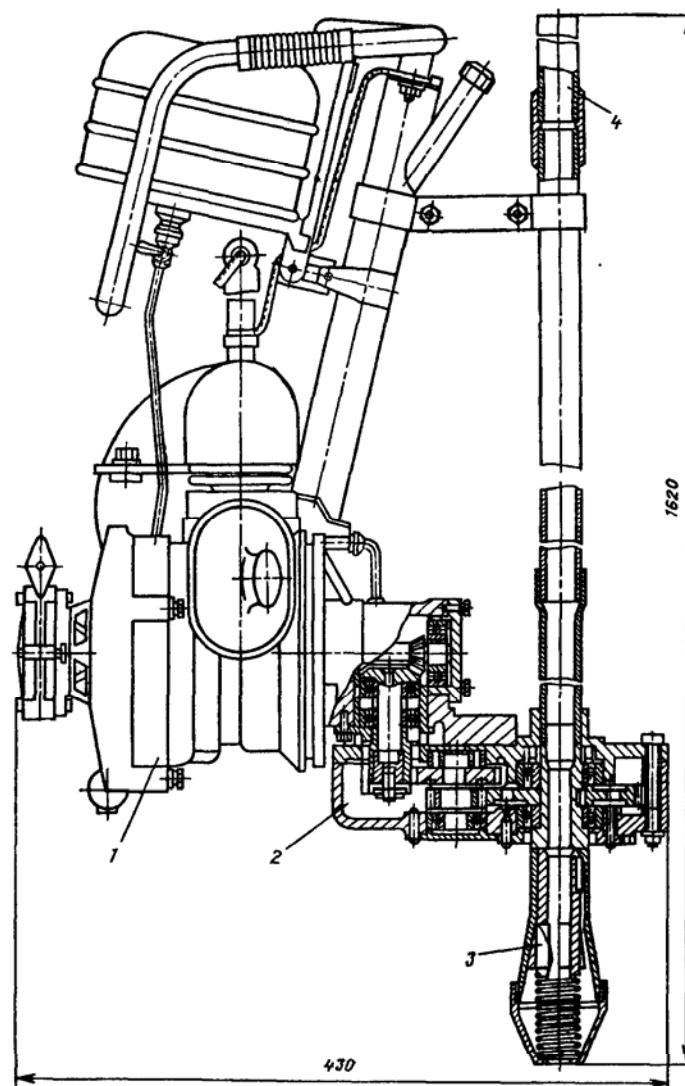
Приспособление ПЗД для ввертывания электродов заземления:
